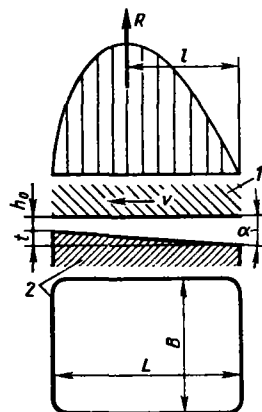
Схема подпятника с наклонной несущей поверхностью
